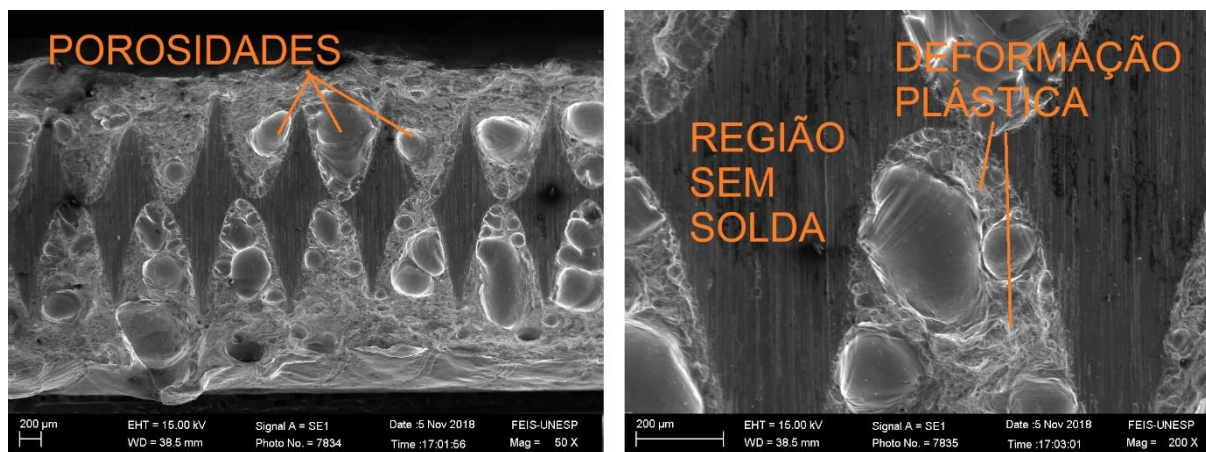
Fratura do cordão de solda da amostra com 50% de taxa de sobreposição.
